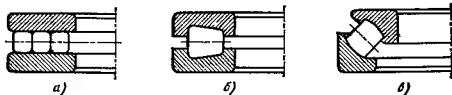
Роликоподшипники упорные конические: а — 9000; б — 19000; в — 39000
